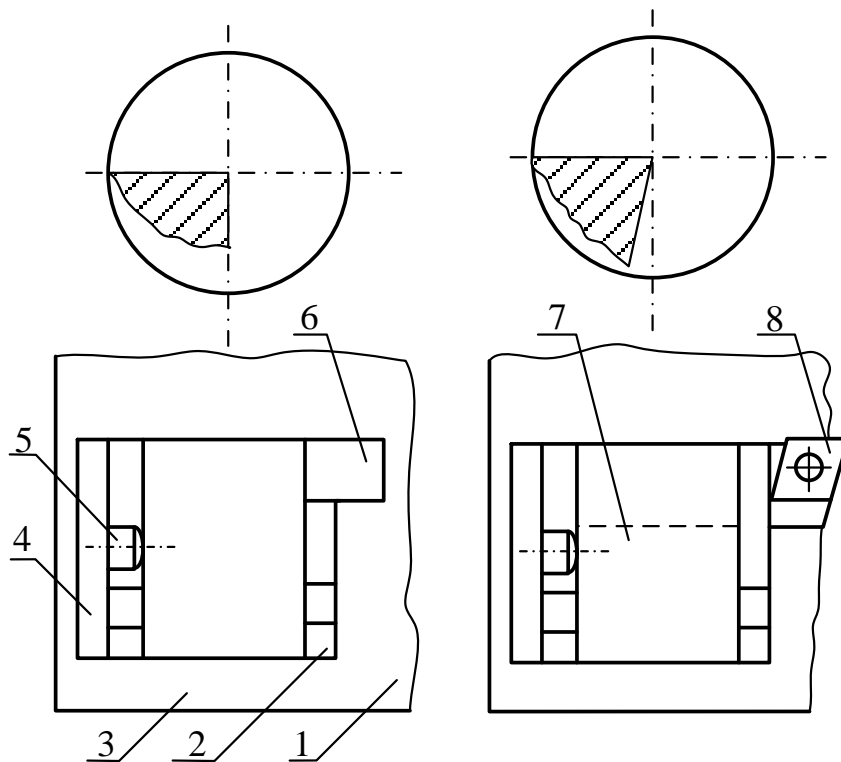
Положение эталона и настраиваемого инструментального блока на приборе мод. 2010: а – положение эталона; б – положение инструментального блока; 1 – стол прибора мод. 2010; 2 – основание привалочной базы; 3, 7 – инструментальные блоки; 4 – стойка привалочной базы; 5 – упор; 6 – шаблон; 8 – сменная многогранная пластина
